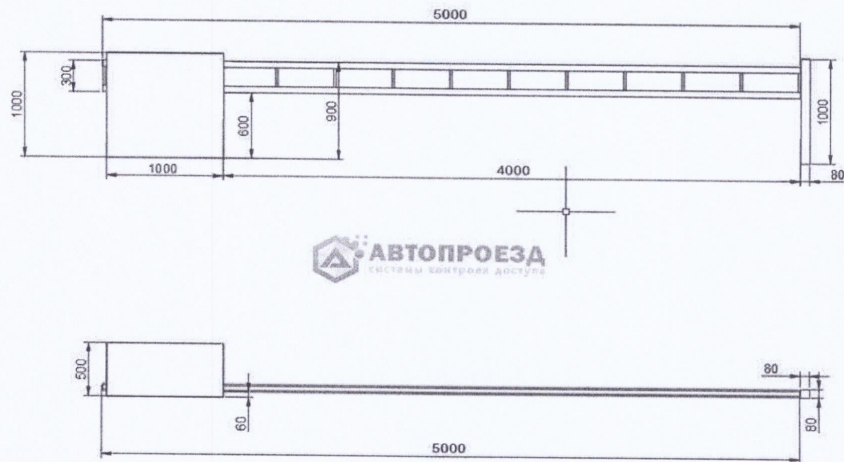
Чертеж размеров шлагбаума № 2
